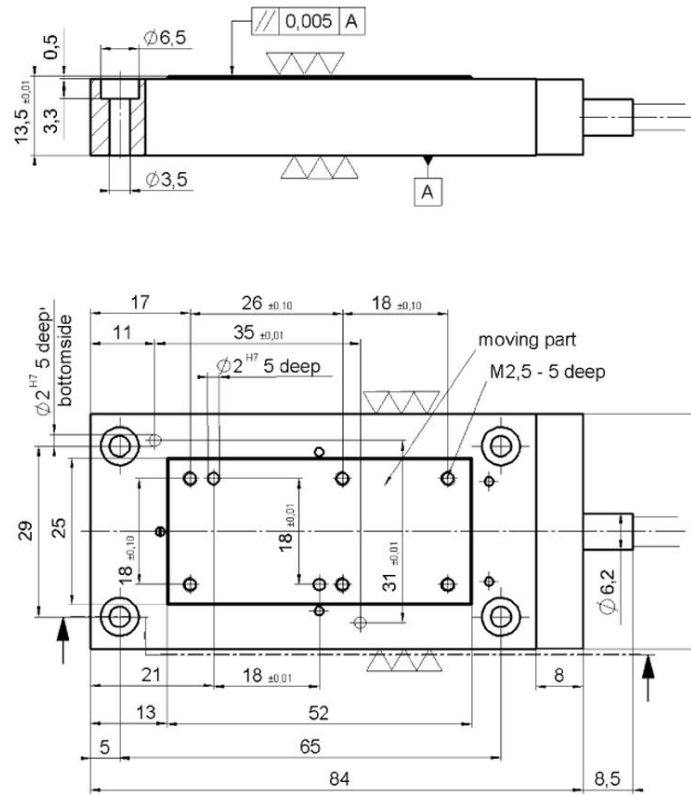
Габаритный чертёж P-752.2xx. Размеры указаны в мм.
